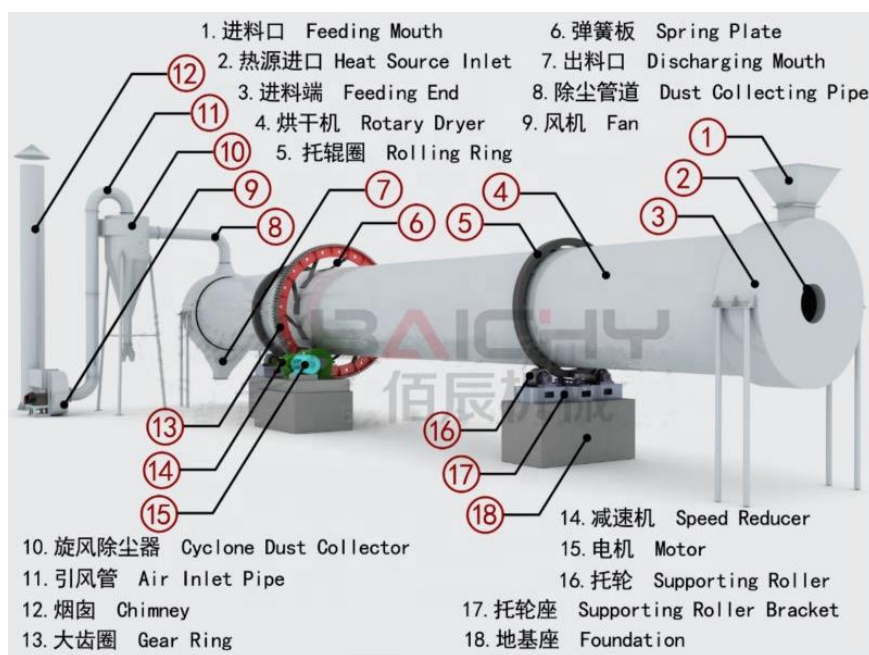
Secador de tambor rotativo para biomasa, del proveedor Henan Baichy Machinery. Fuente: baichy.en.alibaba.com.
